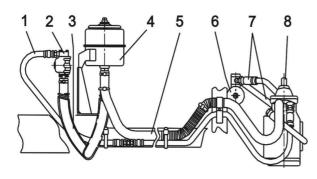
Схема системы гидроусилителя руля 1, 7— шланги высокого давления; 2— насос ГУР с клапанами; 3, 5— шланг низкого давления; 4— бачок; 6— силовой цилиндр; 8— рулевой механизм
